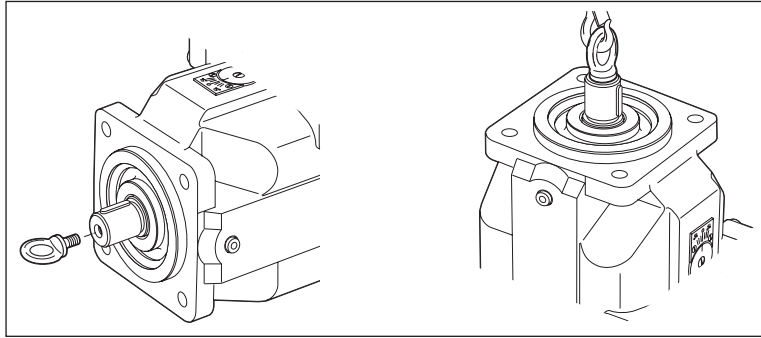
Befestigung der Ringschraube in der Triebwelle
